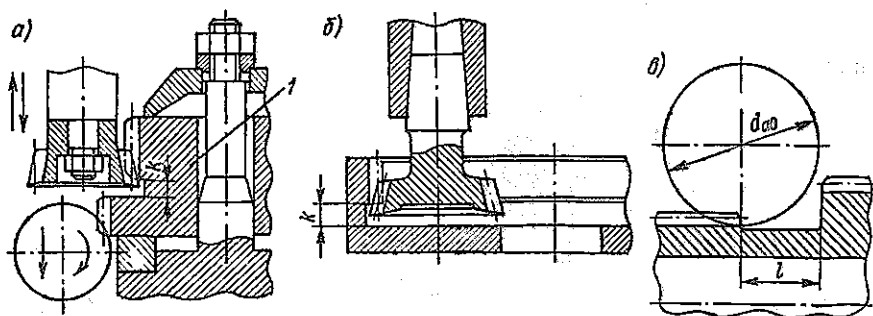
Выход зубообрабатывающего инструмента: а, б — при нарезании долбяком; в — при нарезании блочных зубчатых колес червячной фрезой
